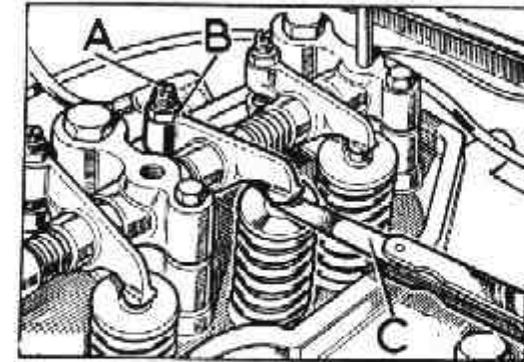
El juego de taqués debe ser de 0,25 mm.
